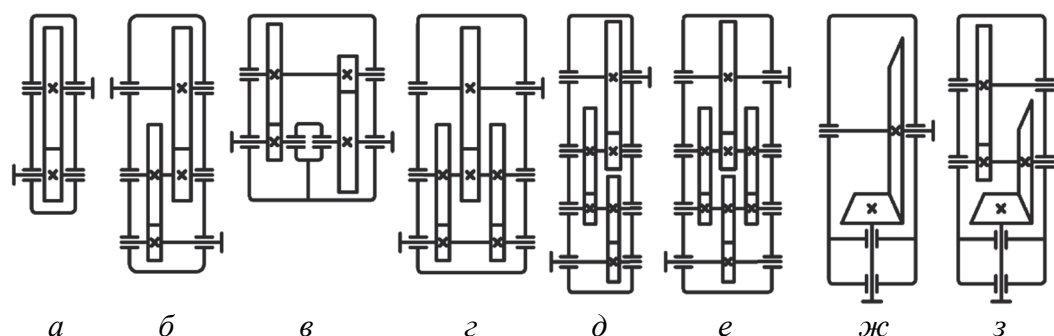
Кинематические схемы цилиндрических и конических редукторов: а – цилиндрический одноступенчатый; б – цилиндрический двухступенчатый по развернутой схеме; в – цилиндрический двухступенчатый соосный; г – цилиндрический двухступенчатый с раздвоенной быстроходной ступенью; д – цилиндрический трехступенчатый по развернутой схеме; е – цилиндрический трехступенчатый с раздвоенной промежуточной ступенью; ж – конический одноступенчатый; з – двухступенчатый коническо-цилиндрический
